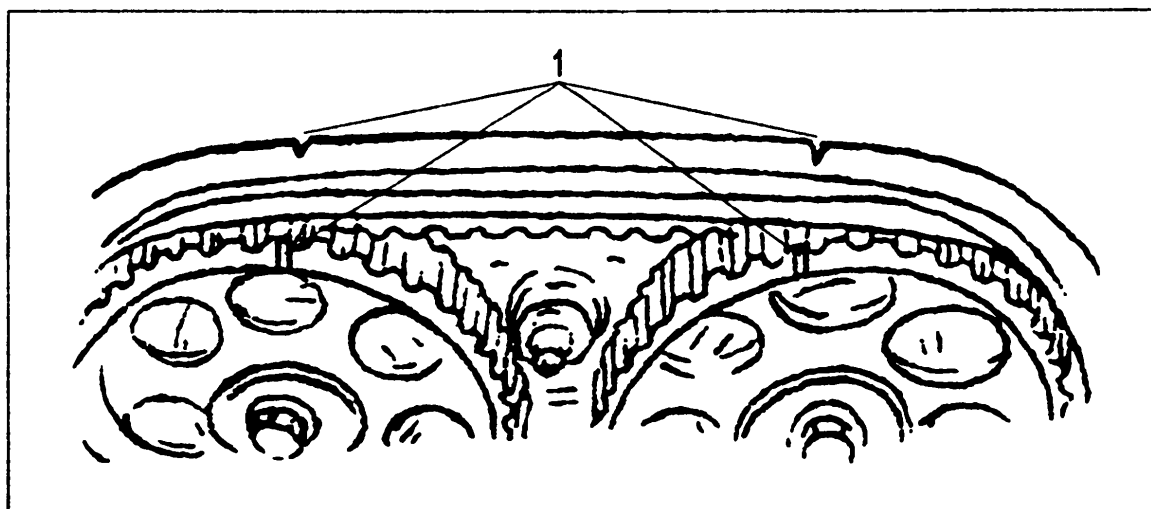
Метки на шестернях распредвала 16-клапанного двигателя совпадают с метками на головке блока цилиндров (1)
